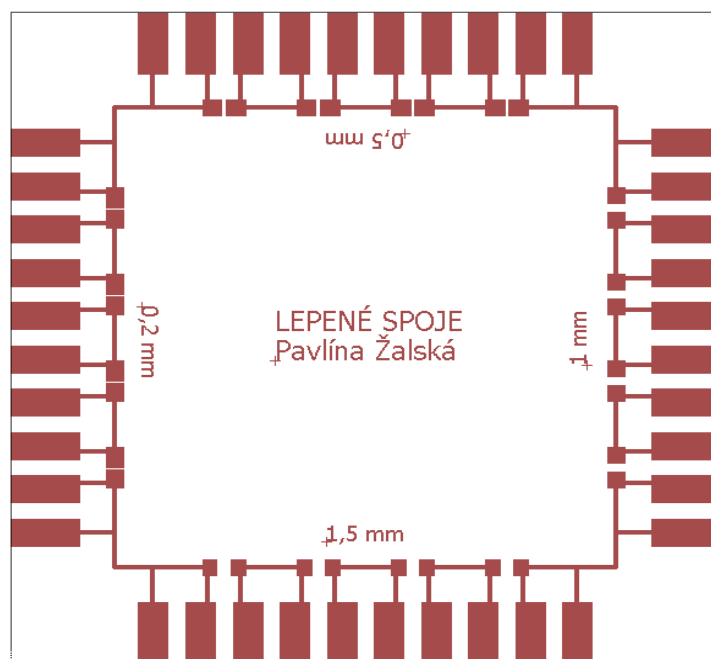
Layout testovací desky určené pro osazení součástkami v první části měření
